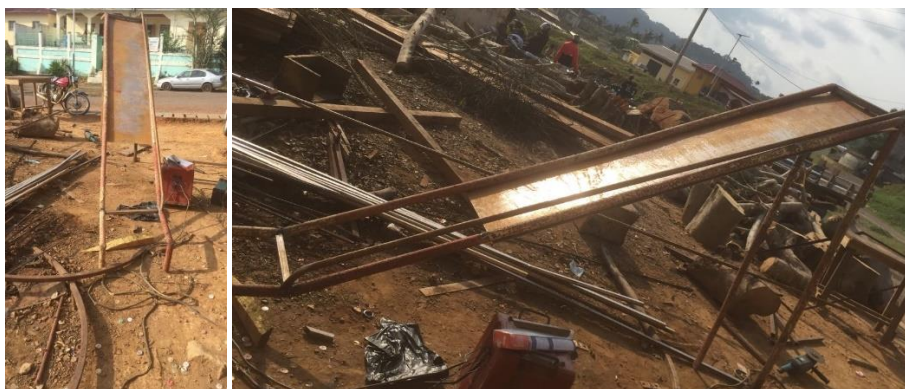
Proceso soldadura tobogán. Fuente: Propia.
